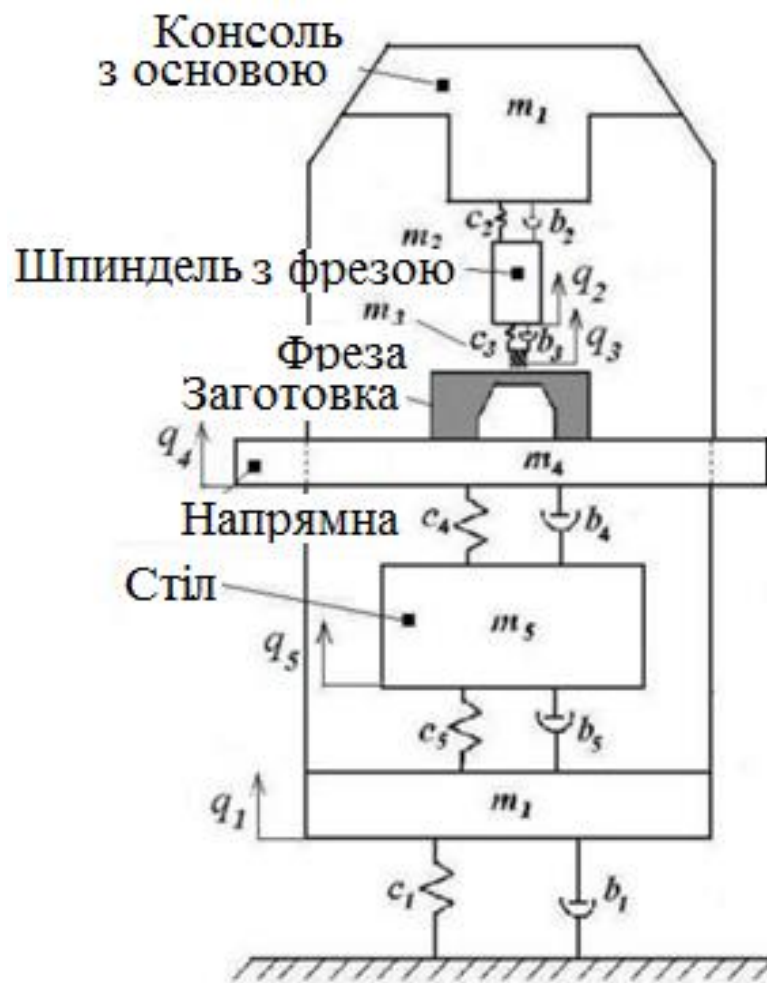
Примірна модель вертикально-фрезерного верстату
